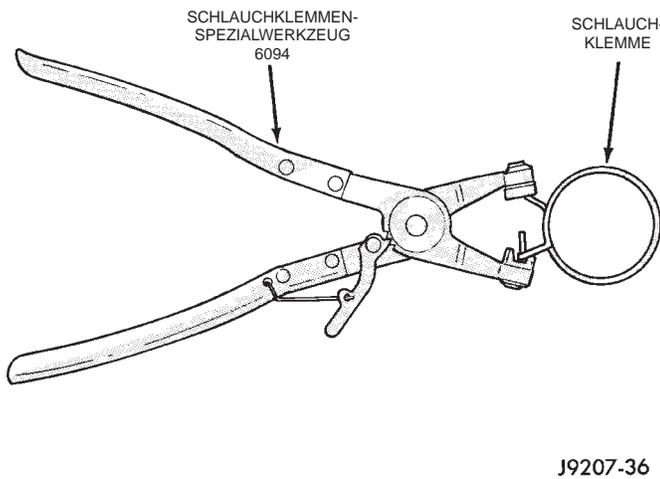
Schlauchklemmen-Spezialwerkzeug—Typisch
